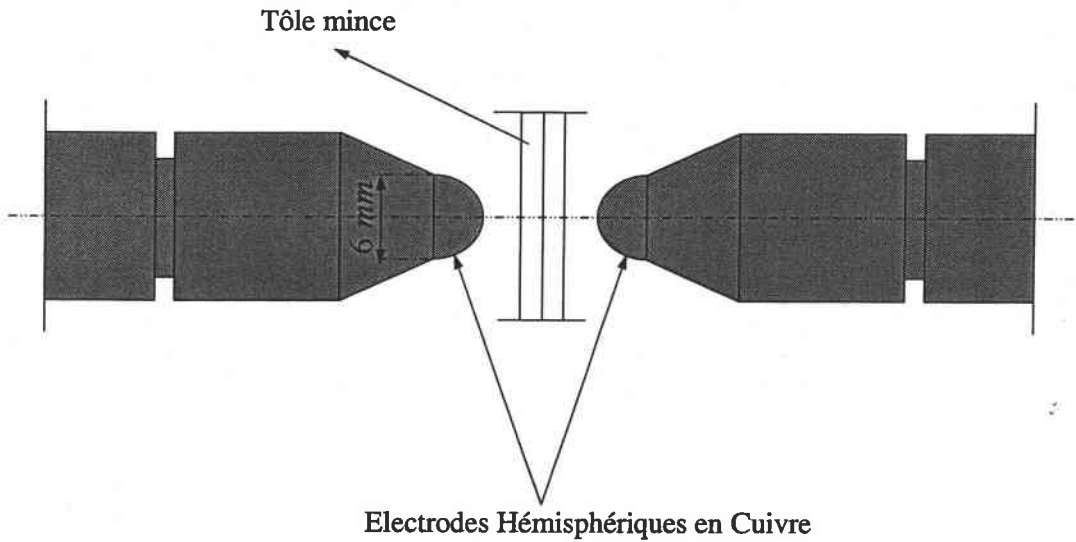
Schéma de l'électrode de soudage hémisphérique appliquée pour des joints soudés par point.
